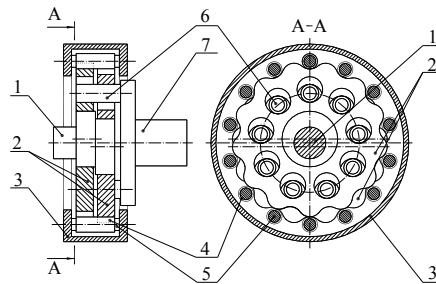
Схема передачи CYCLO Getriebebau: 1) генератор (эксцентрик); 2) кулачки; 3) неподвижное центральное колесо; 4) втулки; 5) оси втулок; 6) пальцы выходного вала; 7) выходной вал
